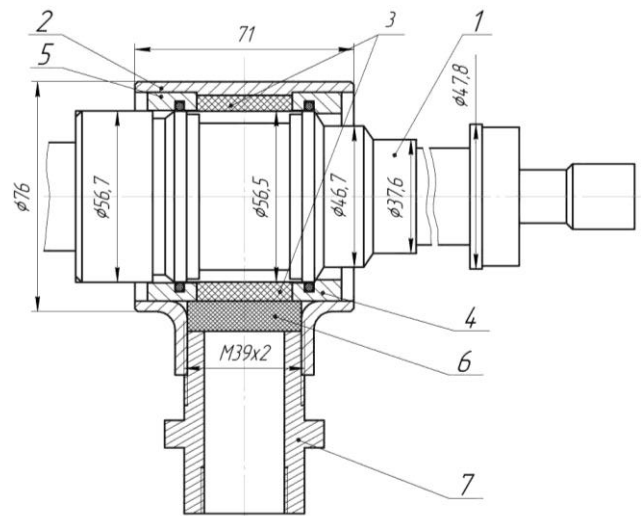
Конструктивная схема глушителя шума пневматической шлифовальной машины
